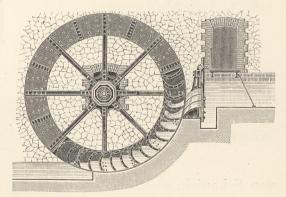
Mittelschlächtiges Wasserrad der Merseburger Maschinenfabrik Herrich & Co.
